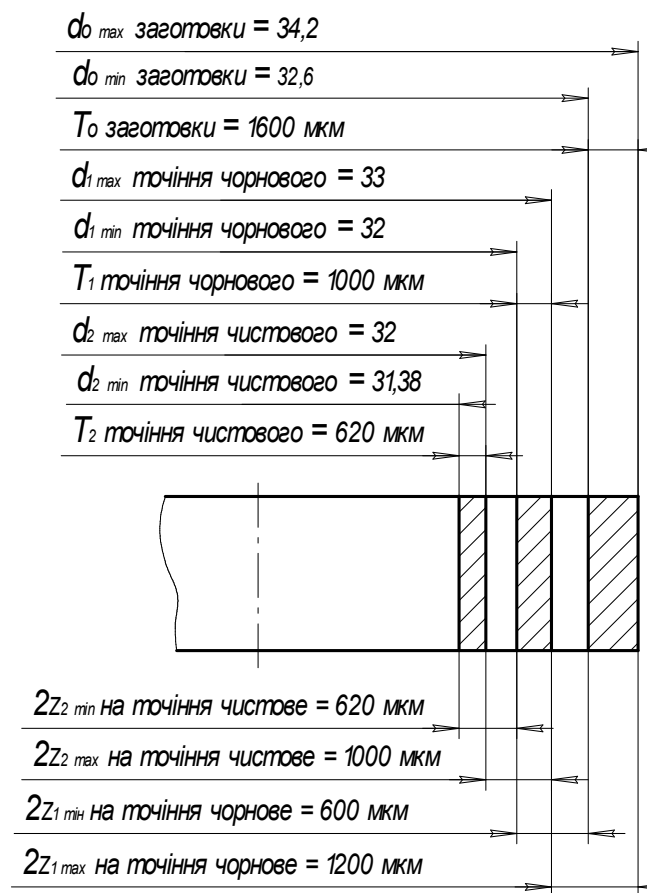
Схема розташування полів припусків і допусків на обробку поверхні $d = 32_{-0.62}$
